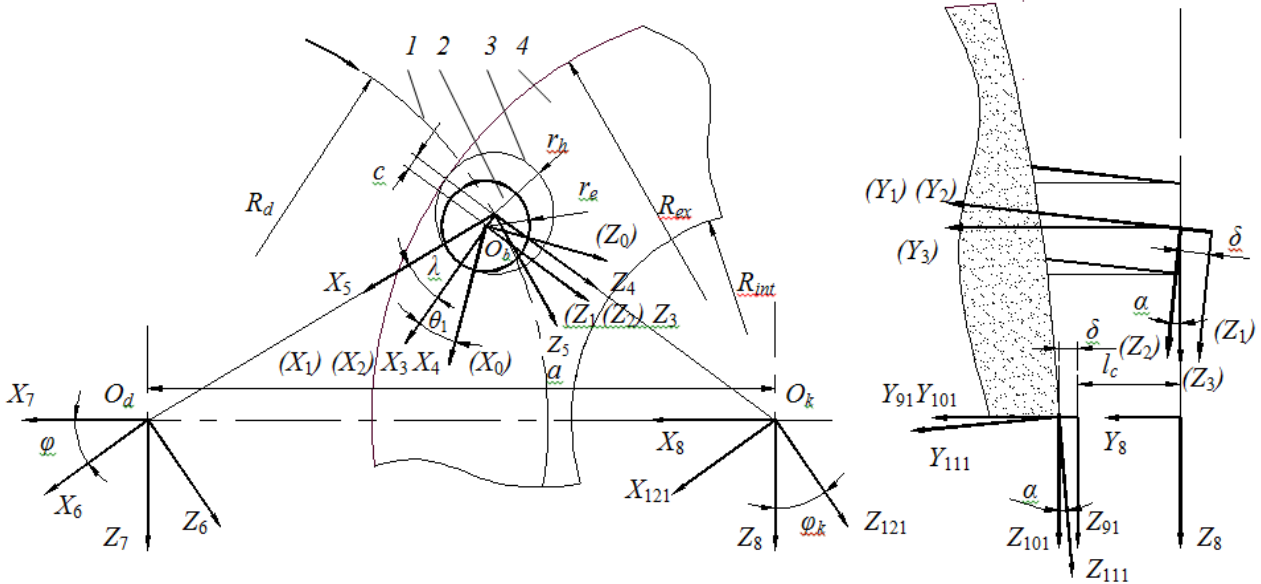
Обобщенная формообразующая система при круговой траектории (1- траектория подачи, 2 – заготовка, 3 – базовая поверхность приспособления, 4 – ШК<sub>1</sub>)
